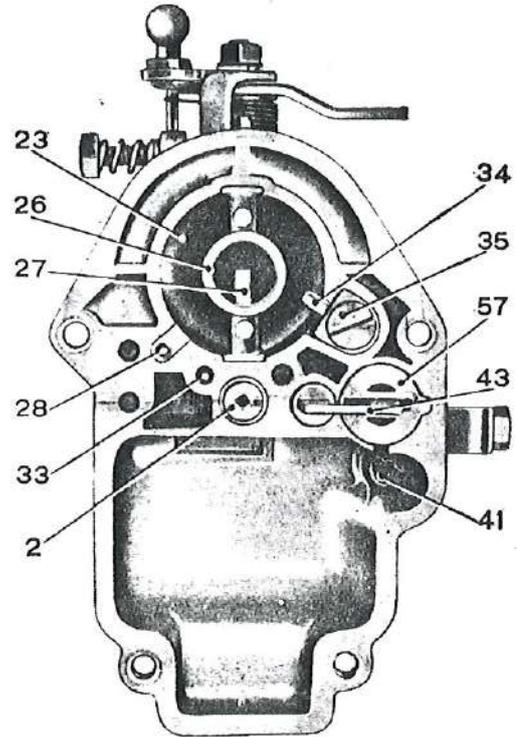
Carburador 28 ICP 6, vista superior, sin tapa.
